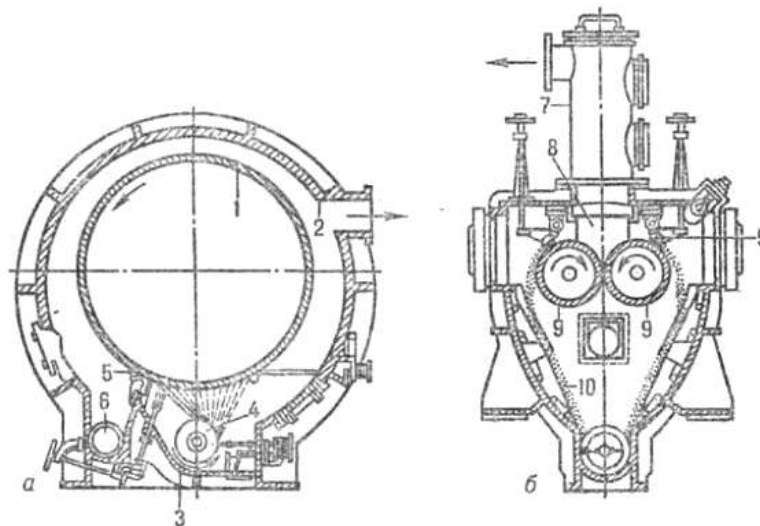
Вальцеві вакуум-сушарки: а – одновальцева; б – двохвальцева; 1 – корпус, 2 – порожнистий барабан (валець), 3 – корито, 4 – розподільчий валик, 5 – ніж, 6 – шнек, 7 – приймальний ковпак, 8 – збірник, 9 – вальці, 10 – похила стіна.
